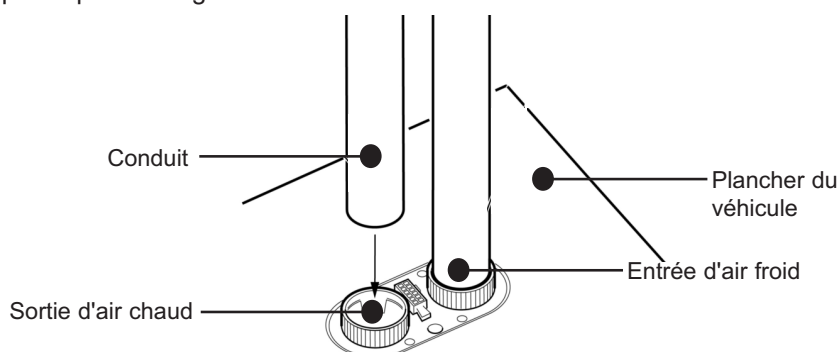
Installation sous plancher - Raccordement au conduit d'air chaud
